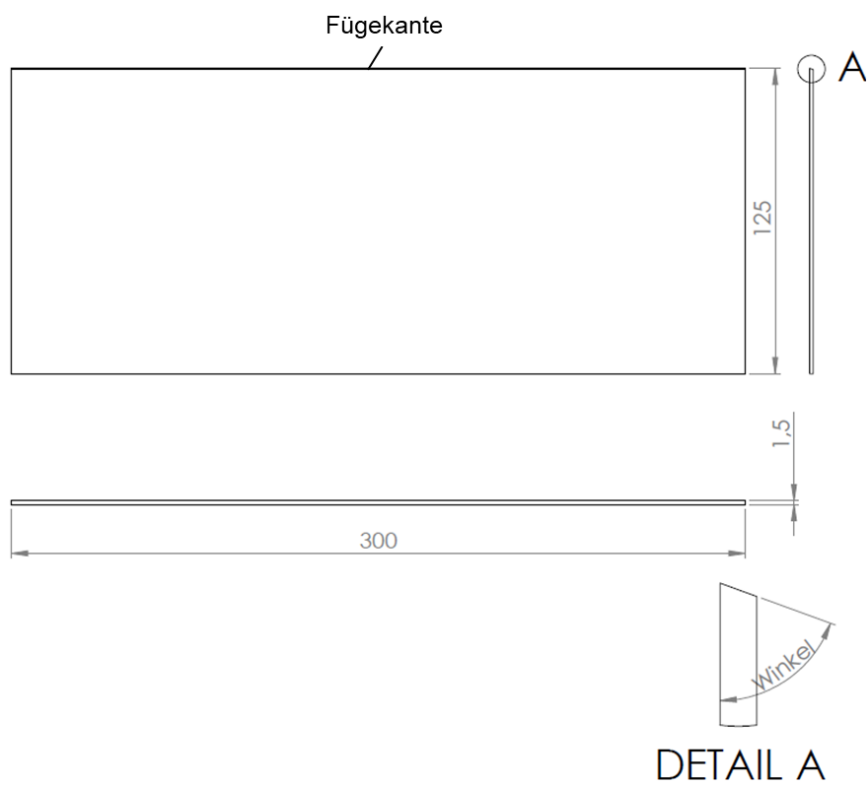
Blech für die Modellversuche zum Laserstrahlschweißen.
